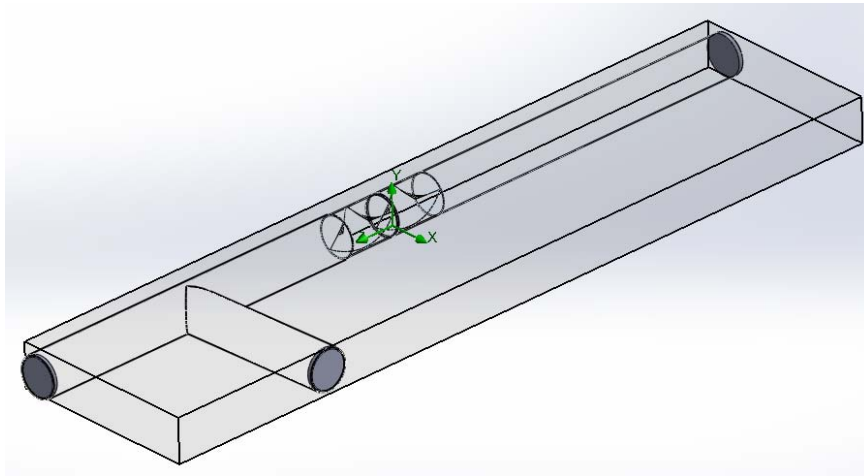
Elemento mezclador incorporado a la "T". Diseño actual.
